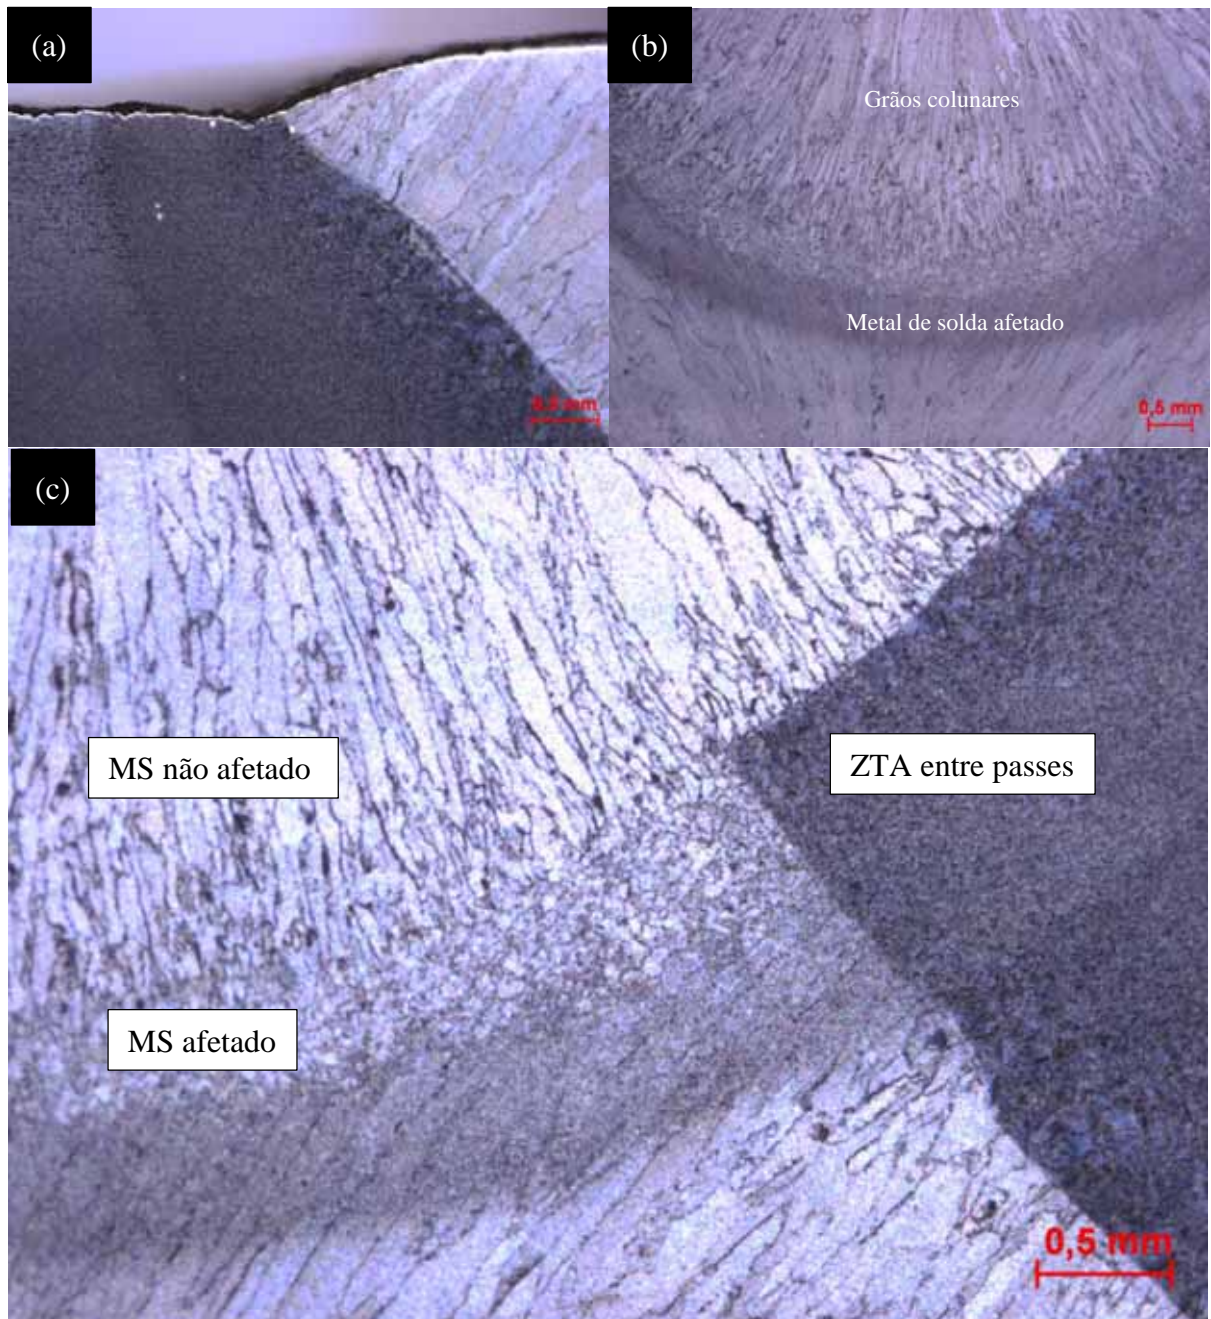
Macrografia da junta soldada formada pelo processo SAW.
